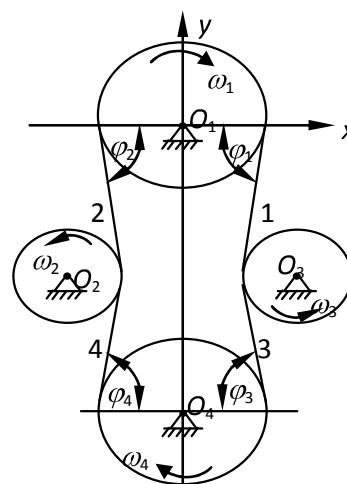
Схема движения ремня механизма с двумя наружными шкивами.
